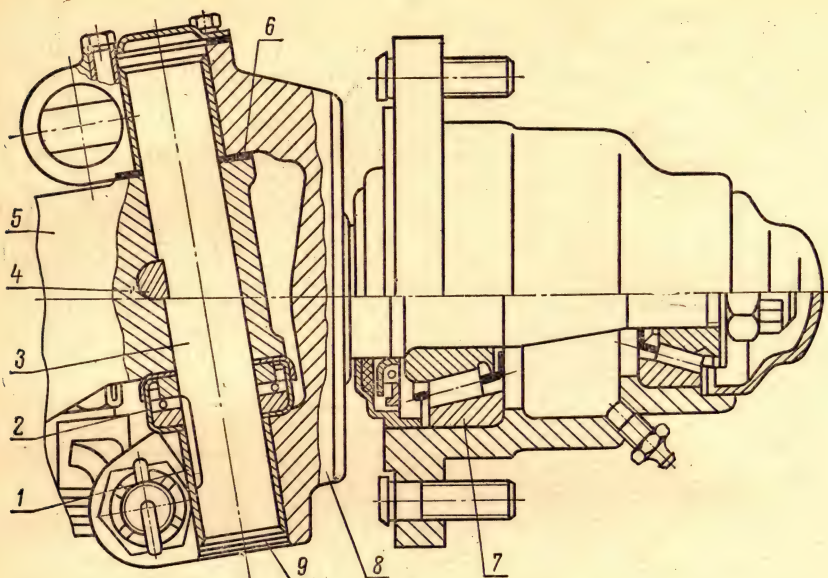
Соединение балки и поворотного кулака с осью управляемых колес:
